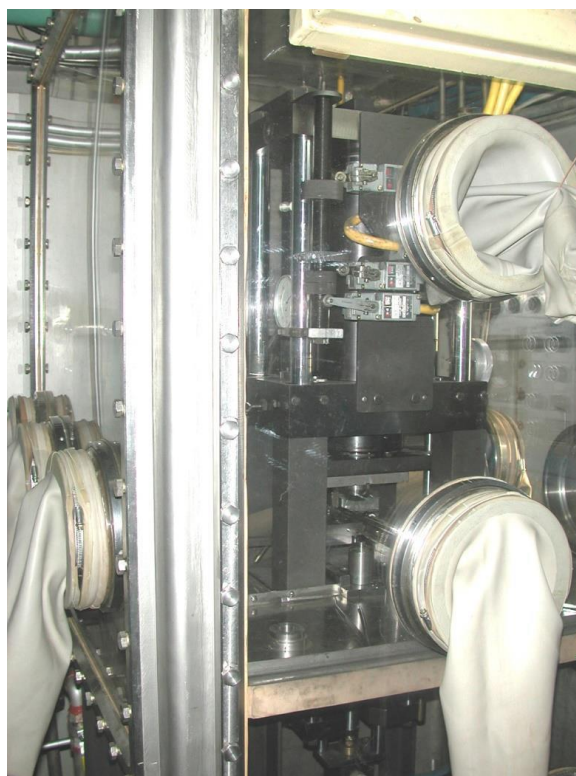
Внешний вид пресса, установленного внутри герметичного перчаточного бокса
